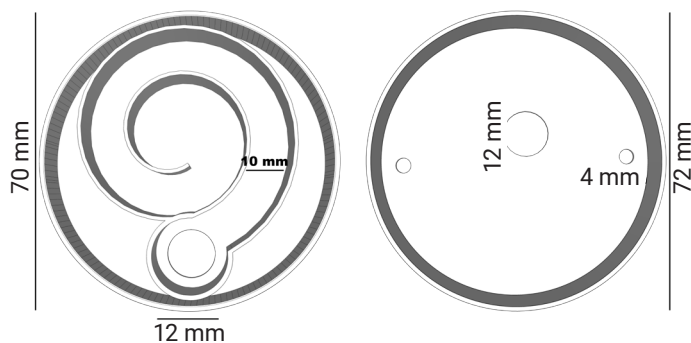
Vista frontal laberinto y tapa. Fuente: Diseño del Autor
